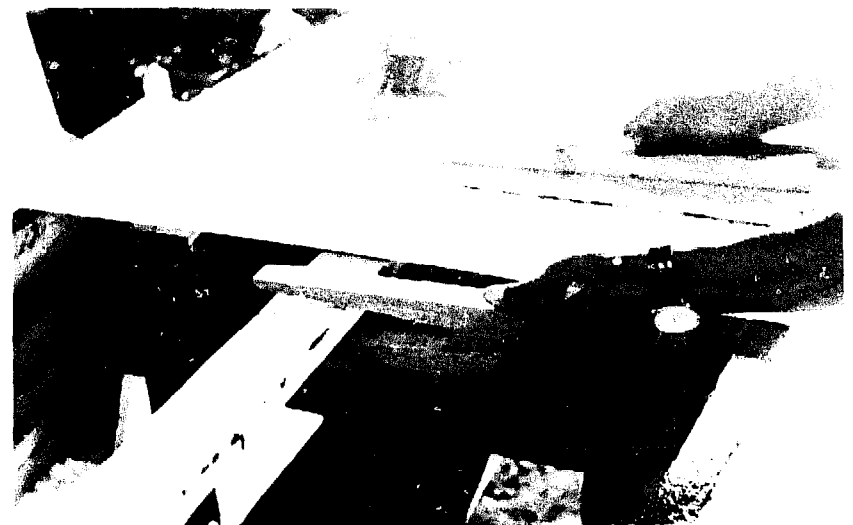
Près de l'autre côté de la planche coincer la serre contre la carlingue
